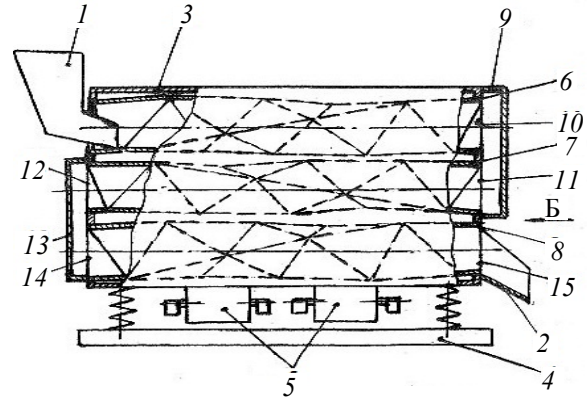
Станок с ярусно расположенными винтовыми роторами
